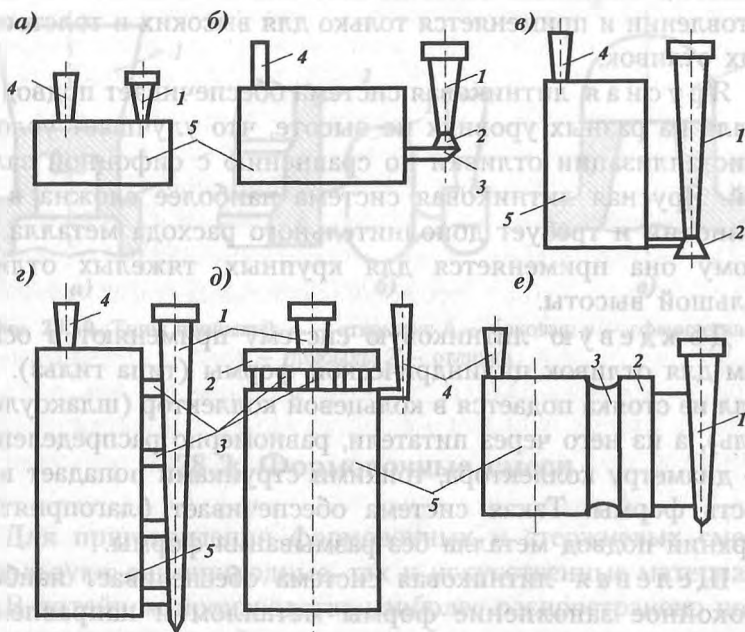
Типы литниковых систем: а — верхняя; б — боковая; в — сифонная; г — ярусная; д — дождевая; е — щелевая; 1 — стояк; 2 — шлакоуловитель; 3 — питатель; 4 — выпор; 5 — отливка
